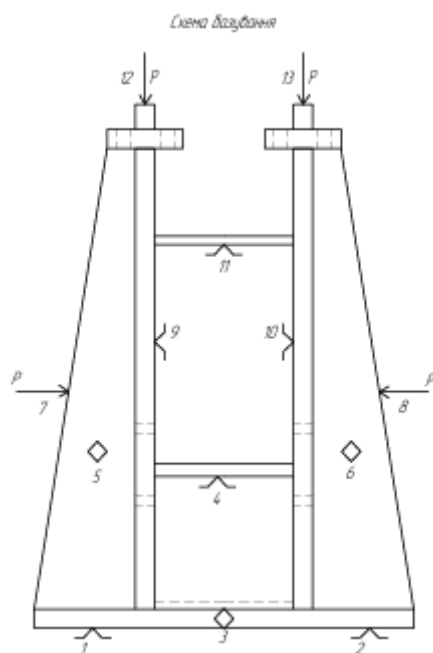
Схема базування рами у складально-зварювальній оснастці
